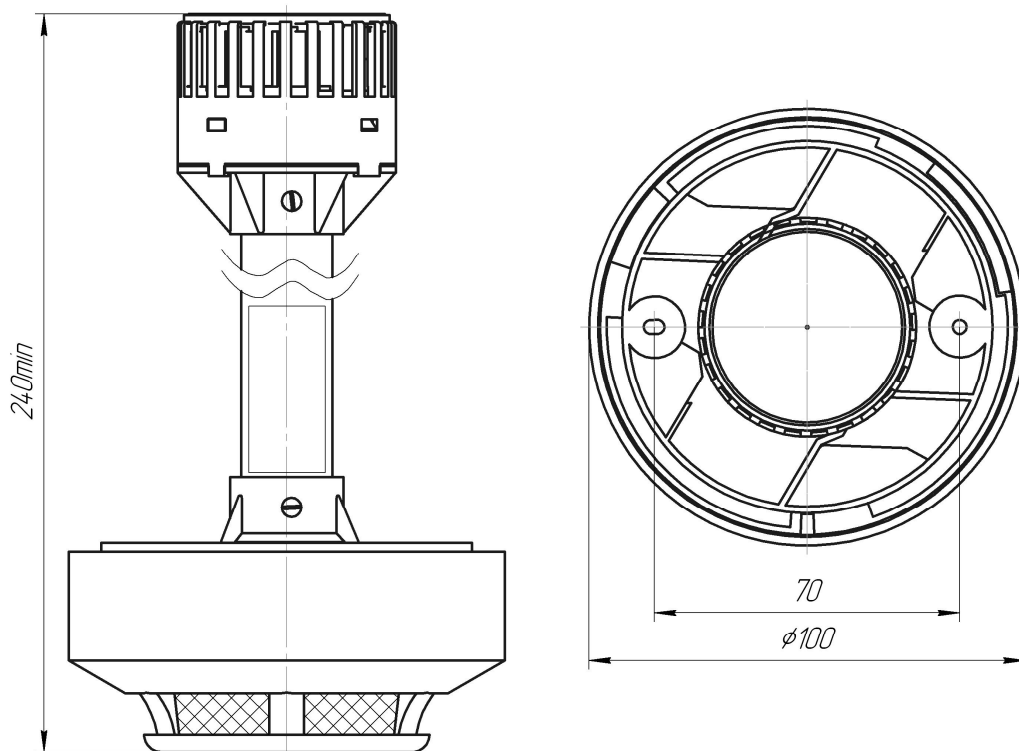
Внешний вид, габаритные и установочные размеры извещателей ИПДОТА-1 (исполнение IP30).
